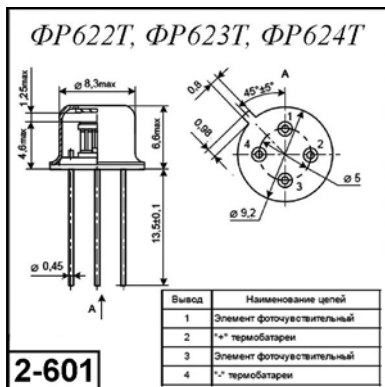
Внешний вид и габаритные размеры охлаждаемых фоторезисторов на основе сульфида свинца
